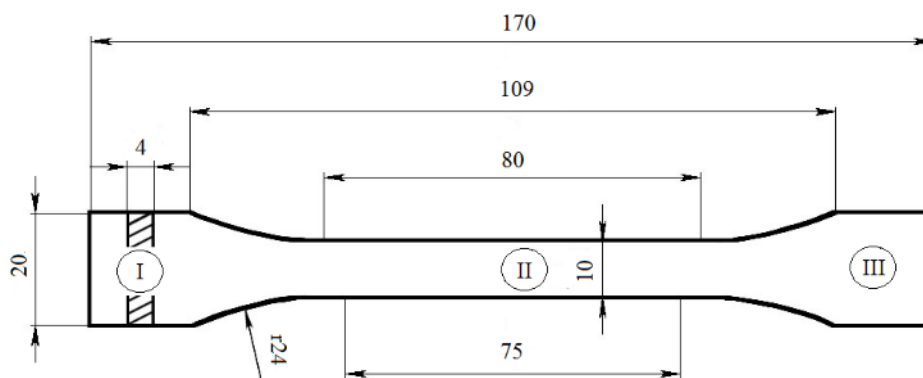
Полимерный образец «Лопатка» и зоны проведения замеров шероховатости поверхности отливки
